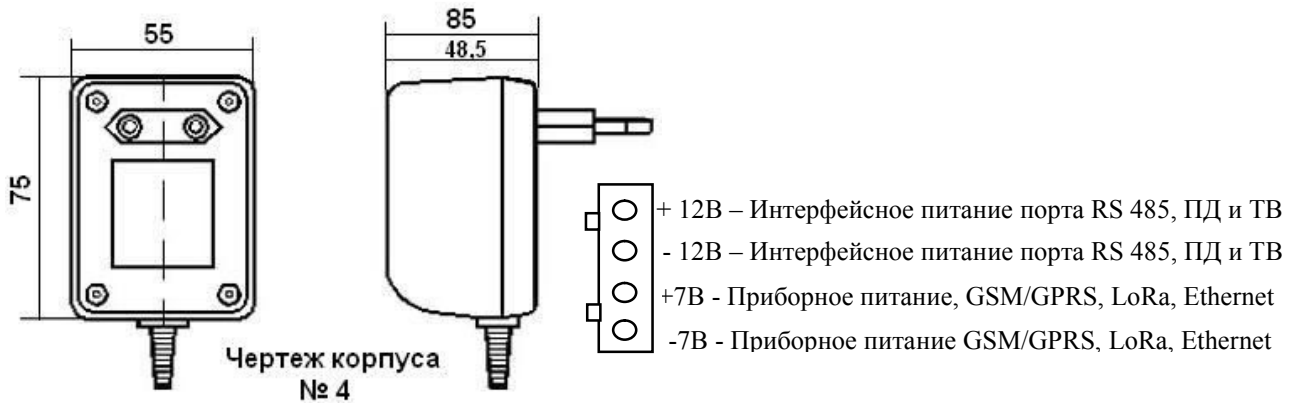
Размеры корпуса источника питания БП-6.
